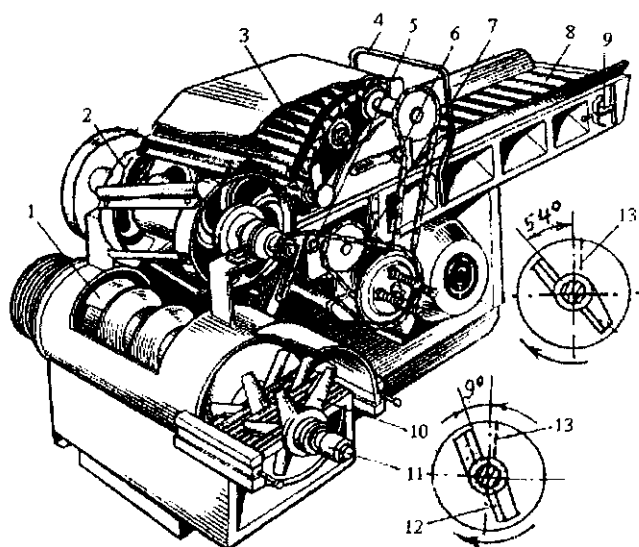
Измельчитель кормов "Волгарь-5": 1-шнек; 2-аппарат первичного резания; 3-уплотняющий транспортёр; 4-скоба управления; 5, 6, 7 - натяжные звёздочки; 8-подающий транспортёр; 9-натяжное устройство подающего транспортёра; 10-аппарат вторичного резания; 11-автомат отключения мотора; 12-лезвие ножа; 13-конец витка шнека.
